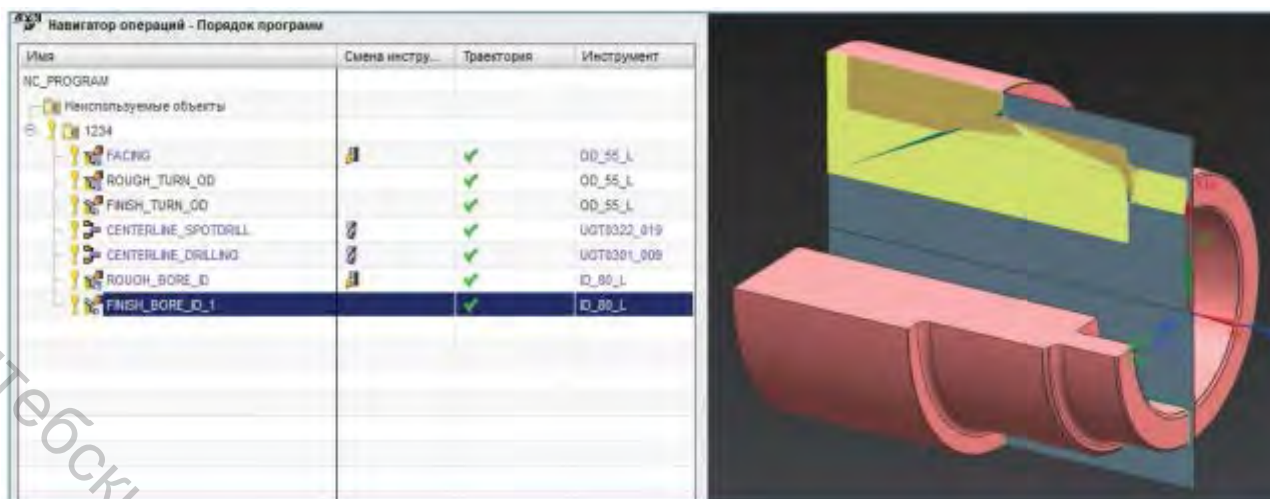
Порядок программ токарной обработки заготовки в главном шпинделе и её сечение с обработанными поверхностями
